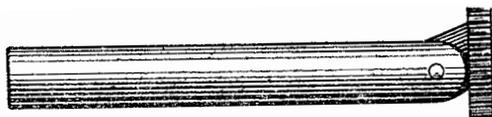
Шпилька для снятия и установки верхних вкладышей коренных подшипников двигателя
